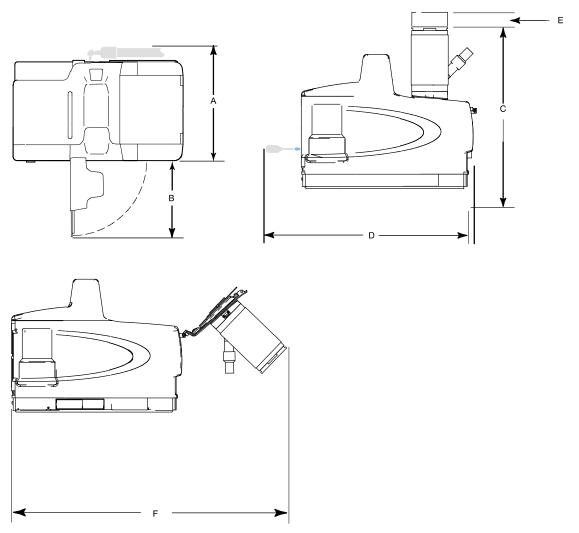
Mindestabstände bei der Installation (Draufsicht und Seitenansicht; siehe Tabelle 1)
